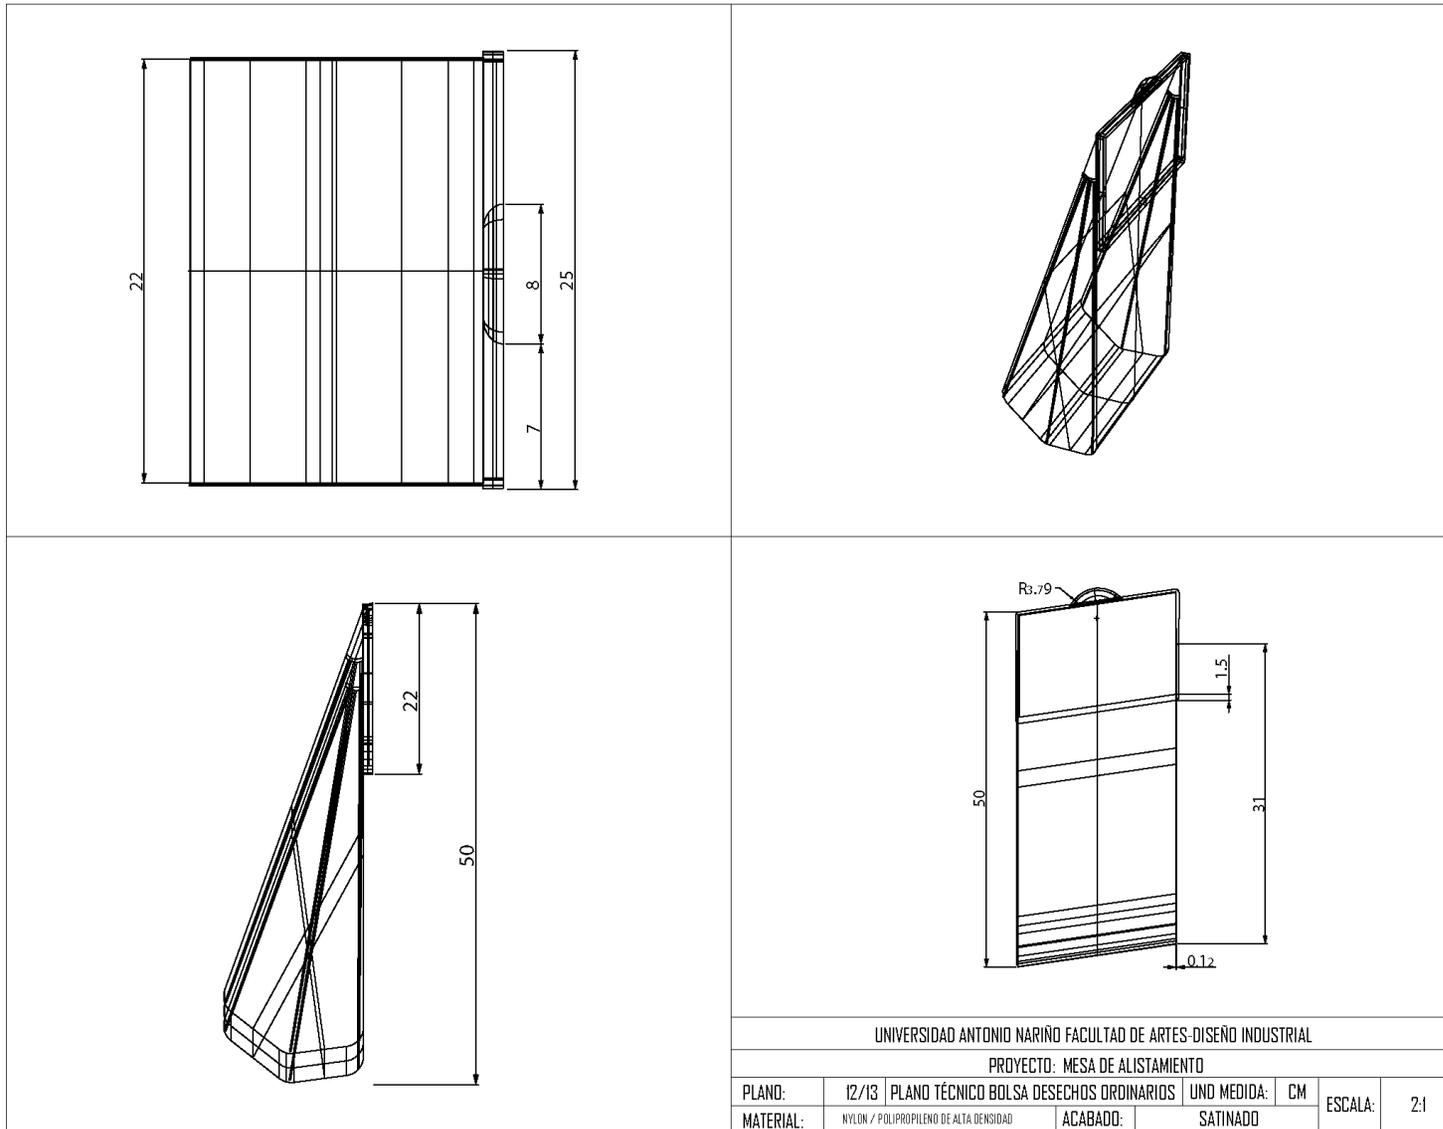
Planos piezas 11 (Elaboración propia, 2020)
